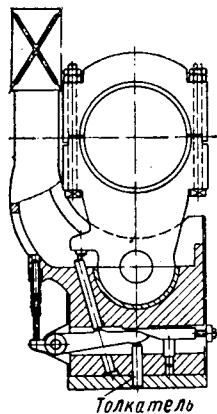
Верхний выталкиватель прессы с толкателем от шпильки.
